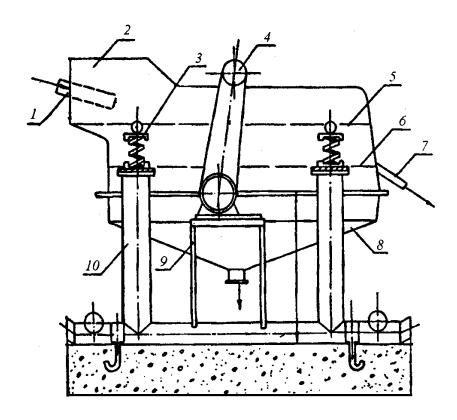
Схема установки виброфильтра: 1 - распределительный лоток; 2 - короб; 3 - амортизатор; 4 - вибратор; 5 - сито верхнее; 6 - сито нижнее; 7 - лоток отвода твердой фракции; 8 - поддон; 9 - электродвигатель; 10 - поддерживающая рама.
